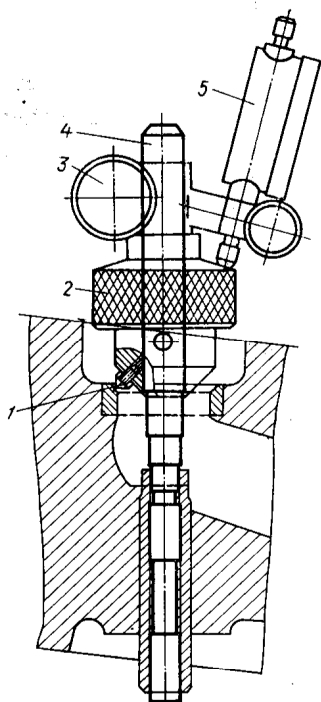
Приспособление для проверки концентричности фаски седла клапана оси направляющей втулки:
